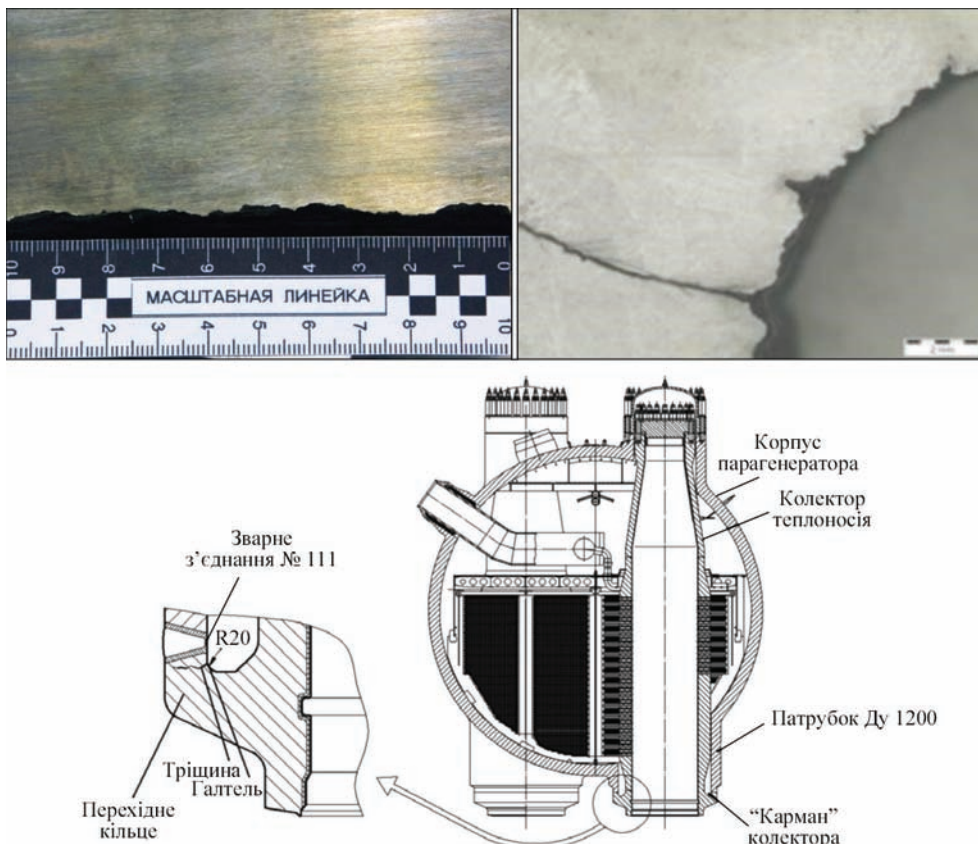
Корозійне руйнування у вузлі зварного з'єднання № 111 колектора до патрубка Ду1200 парогенераторів ПГВ-1000
